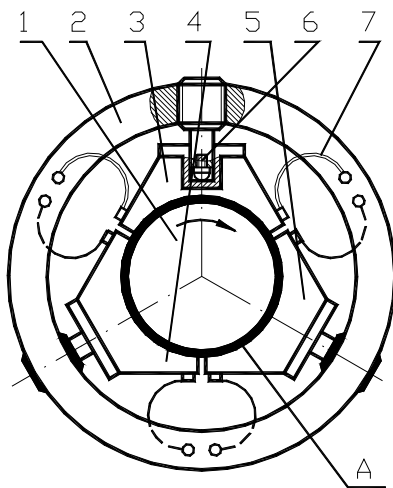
Конструкция газостатического подшипника с самоустанавливающимися сегментами
